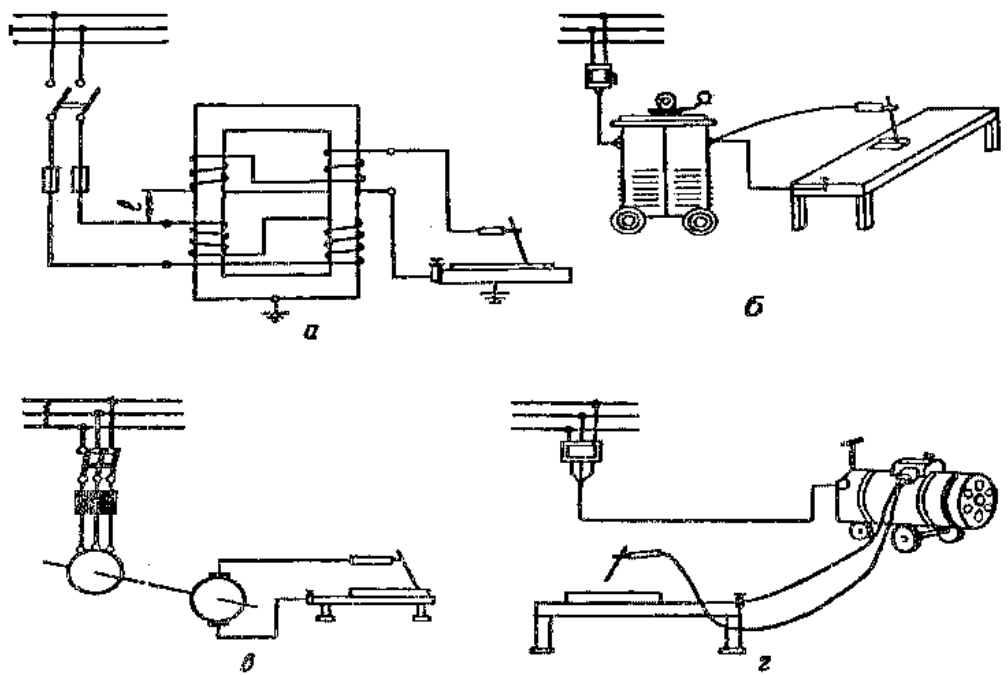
Схемы сварочных постов для ручной сварки
